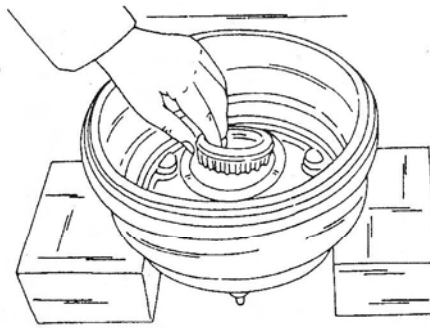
Установка внутреннего колесного подшипника в тормозной барабан.
